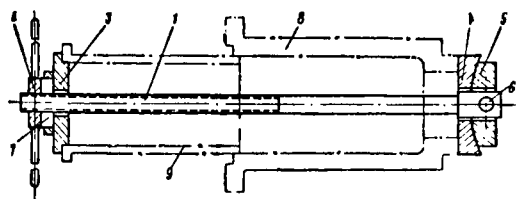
Приспособление для запрессовки втулок цилиндра:
